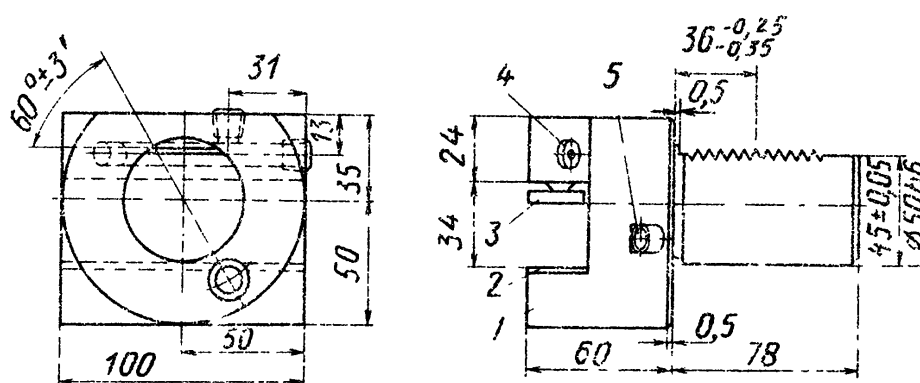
Резцедержатели токарных станков с ЧПУ
